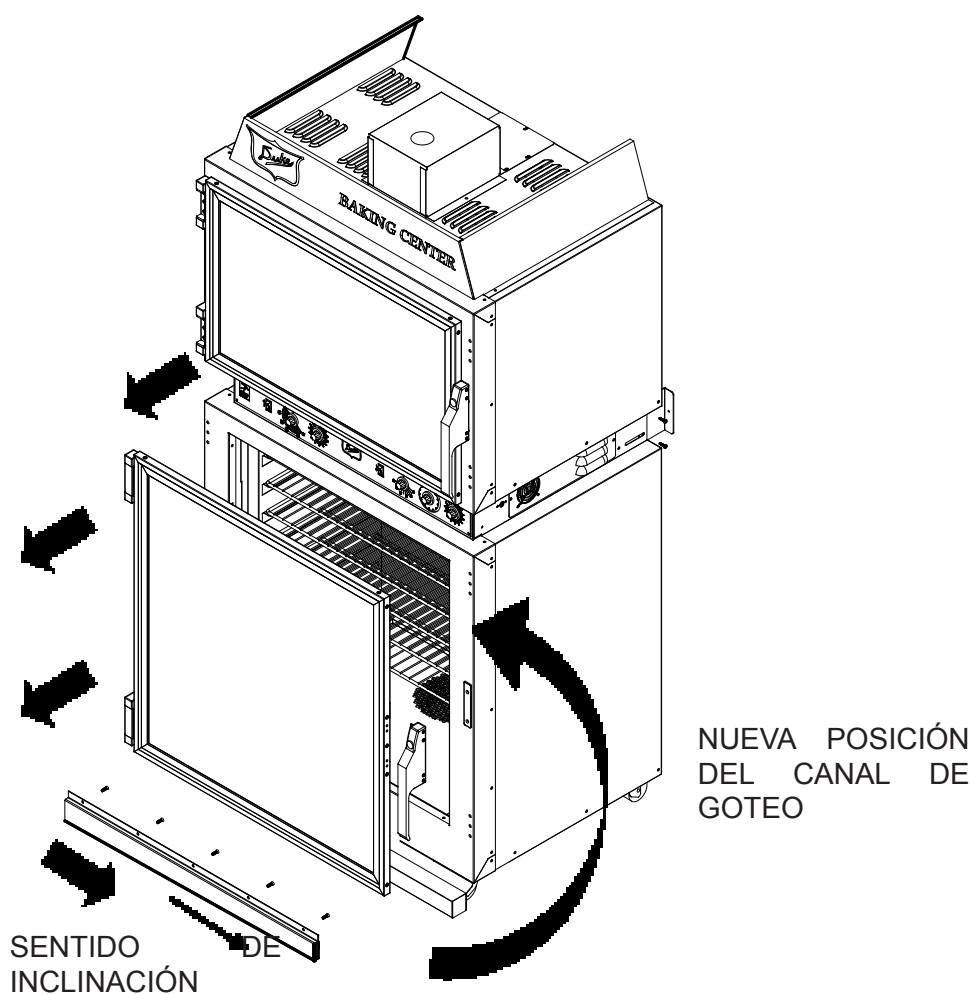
Ilustración – Inversión del sentido de giro de la puerta de la fermentadora
